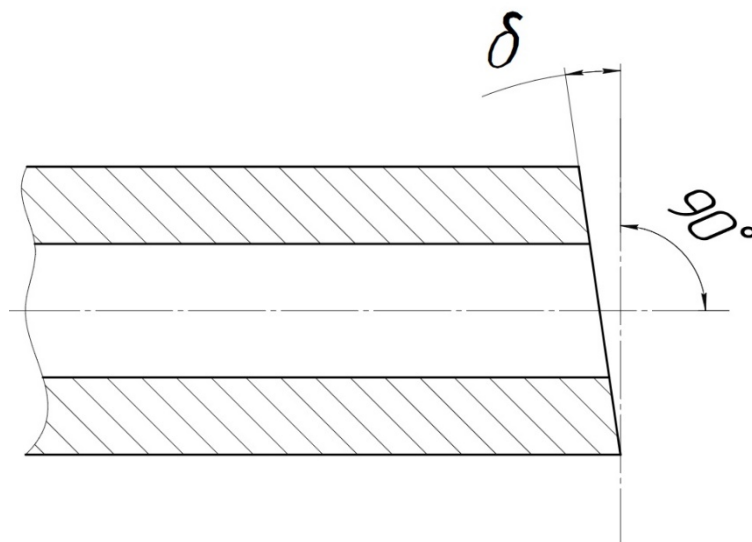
Схема расположения опорного торца обрабатываемой детали
